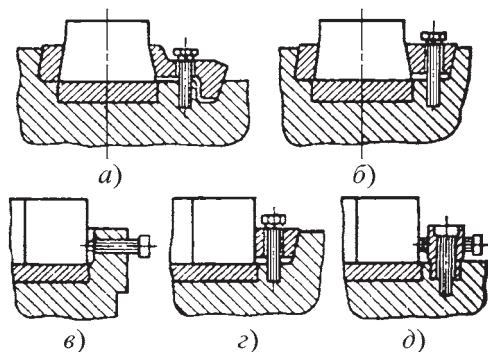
Крепление штамповых вставок в блоке: а — продольное прихватами; б — продольное прижимными клеммами; в — боковое упорными винтами; г — боковое прижимными клеммами; д — упорными винтами через стойку
